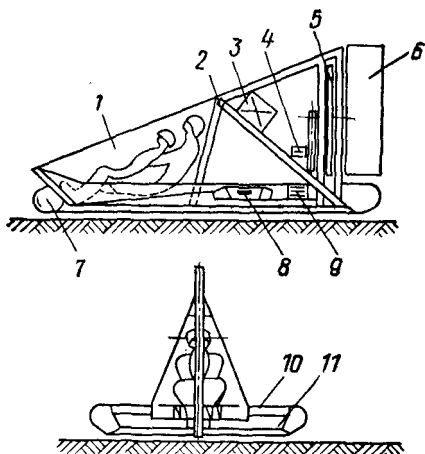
Спортивно-туристический АВП, построенный автором книги. 1—экипаж; 2—каркас; 3—топливный бак; 4—агрегат горизонтальной тяги; 5—воздушный винт; 6—руль направления движения; 7—гибкое ограждение; 8—нагнетатель; 9—двигатель подъемной системы; 10—корпус; 11—поплавок.
